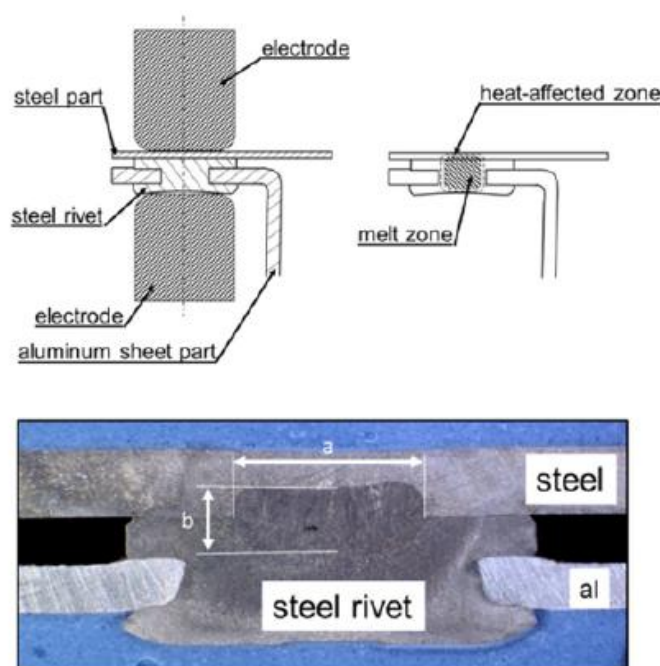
Схема конструкции точек заклепочной сварки
